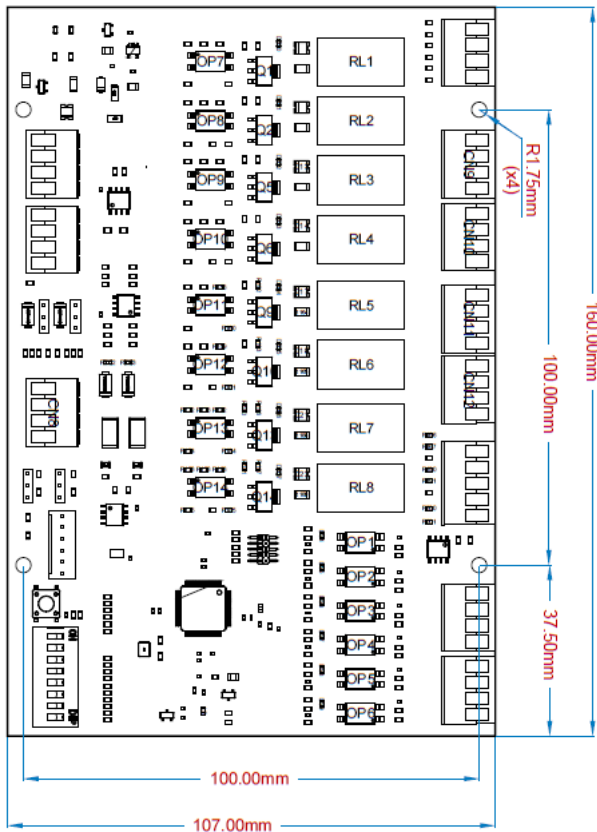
Dimensões mecânicas Flexcard I/O (PR17036)
